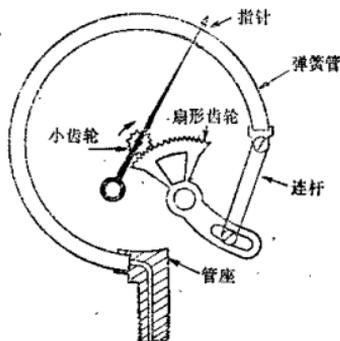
带有传动杠杆(连杆—小齿轮—扇形齿轮)放大机构的C型弹簧管压力表
